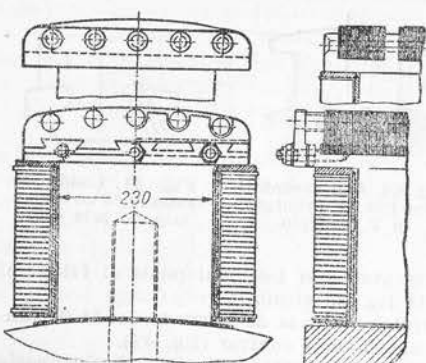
Pol masiv cu piesa polară din tole fixată prin coadă de rândunică.
